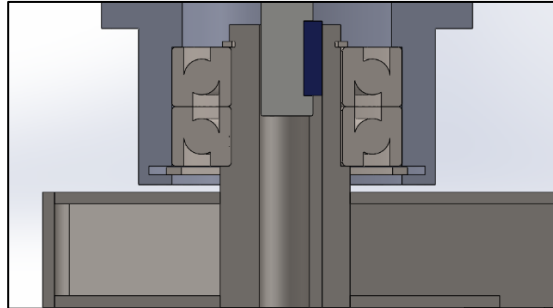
Corte del ensamblaje del módulo de dirección.
